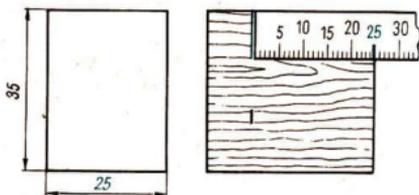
/1 Technische Zeichnung und richtiges Anreißen mit dem Maßstab
